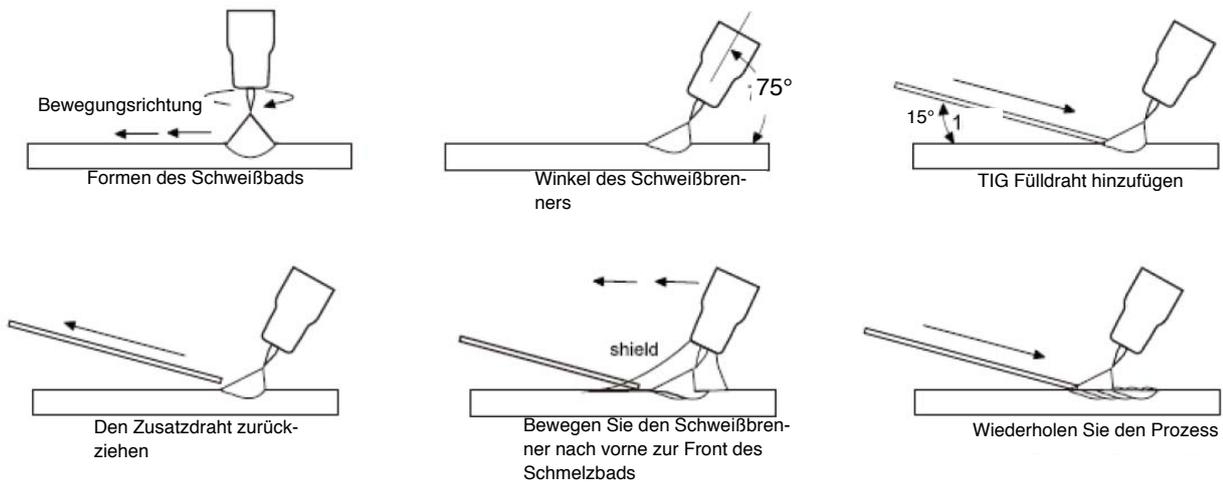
Ablauf des WIG-Schweißens mit Zusatzdraht
